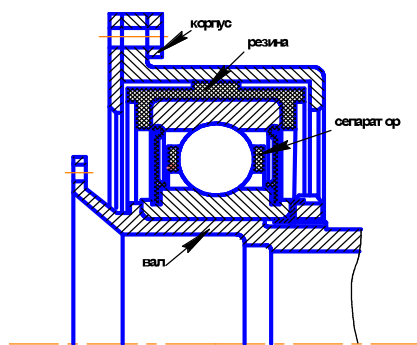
Эскиз подшипникового узла трансмиссии вертолёта с резиновым амортизатором
